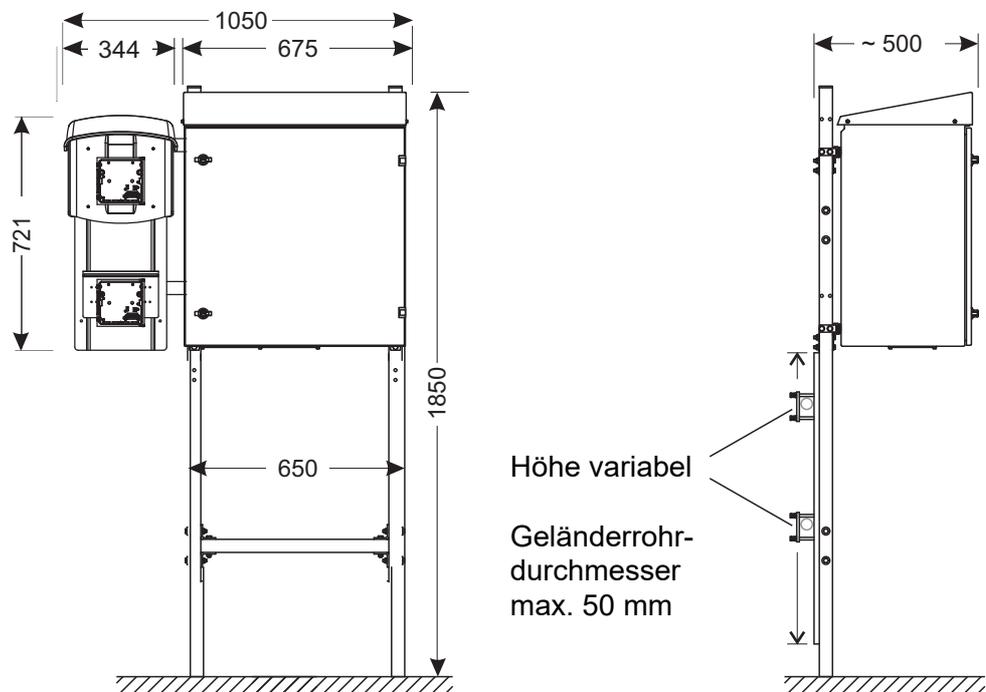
Maßzeichnung Alyza IQ Montage an einem Geländer (Maße in mm)
